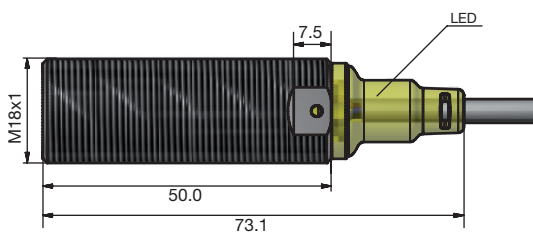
Lange Ausführung, bündiger Einbau, Kabel
